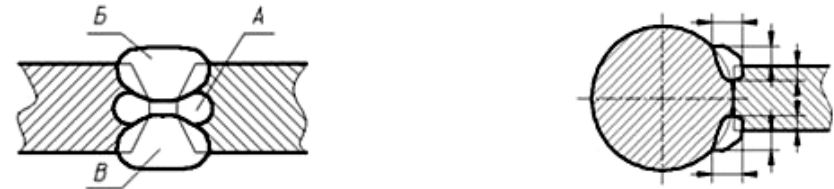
Пример изображения нестандартного сварного шва
